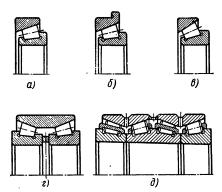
Роликоподшипники с коническими роликами, радиально-упорные: a — однорядный, тип 7000, ГОСТ 333—59; δ — то же с упорным бортом на наружном кольце, тип 67000, ГОСТ 3169—46; ϵ — то же с большим углом конуса, тип 27000, ГОСТ 7260—54; ϵ — двухрядный, тип 97000, ГОСТ 6364—68; δ — четырехрядный, тип 77000, ГОСТ 8419—57
